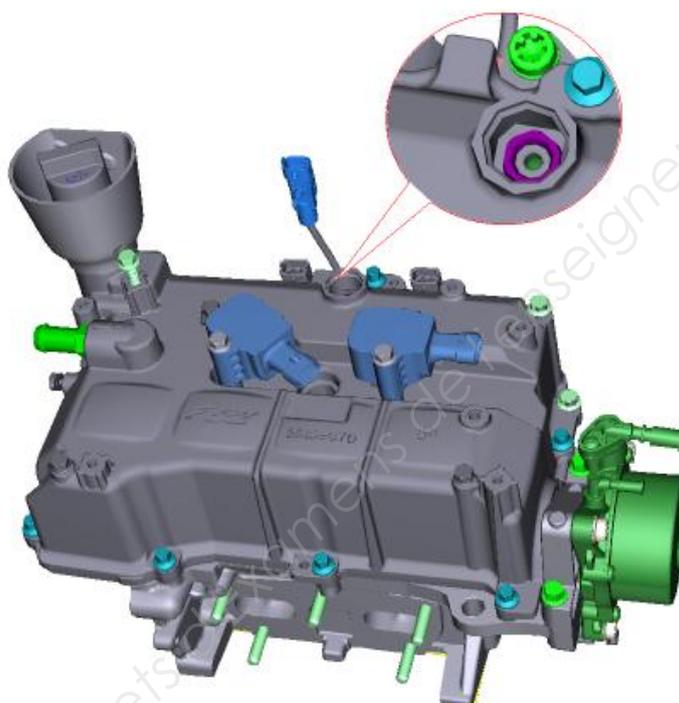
soupape d'introduction d'huile pour le remplissage du module.
